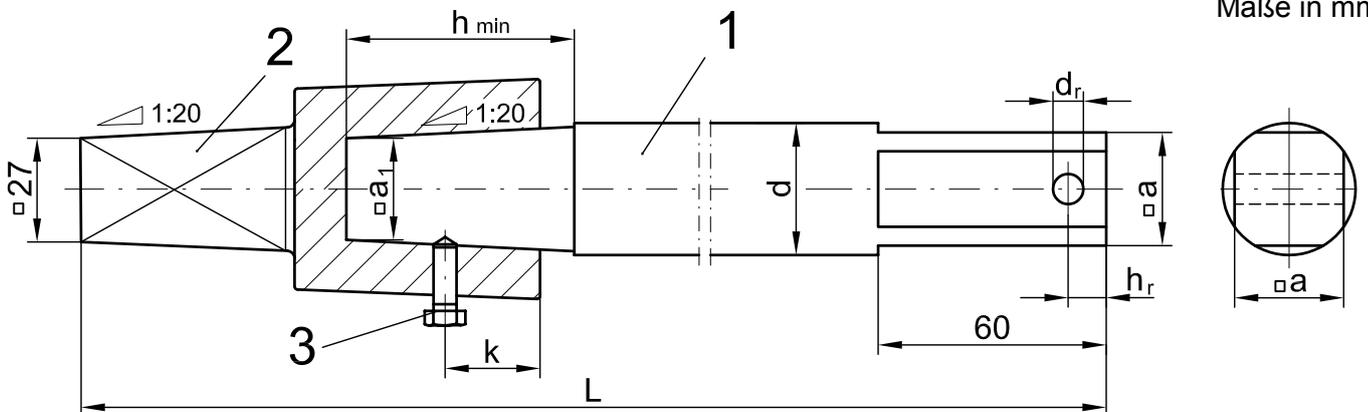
Spindelverlängerung für Schieber DN 250/DN 300 (weich u. metallisch dichtend)
